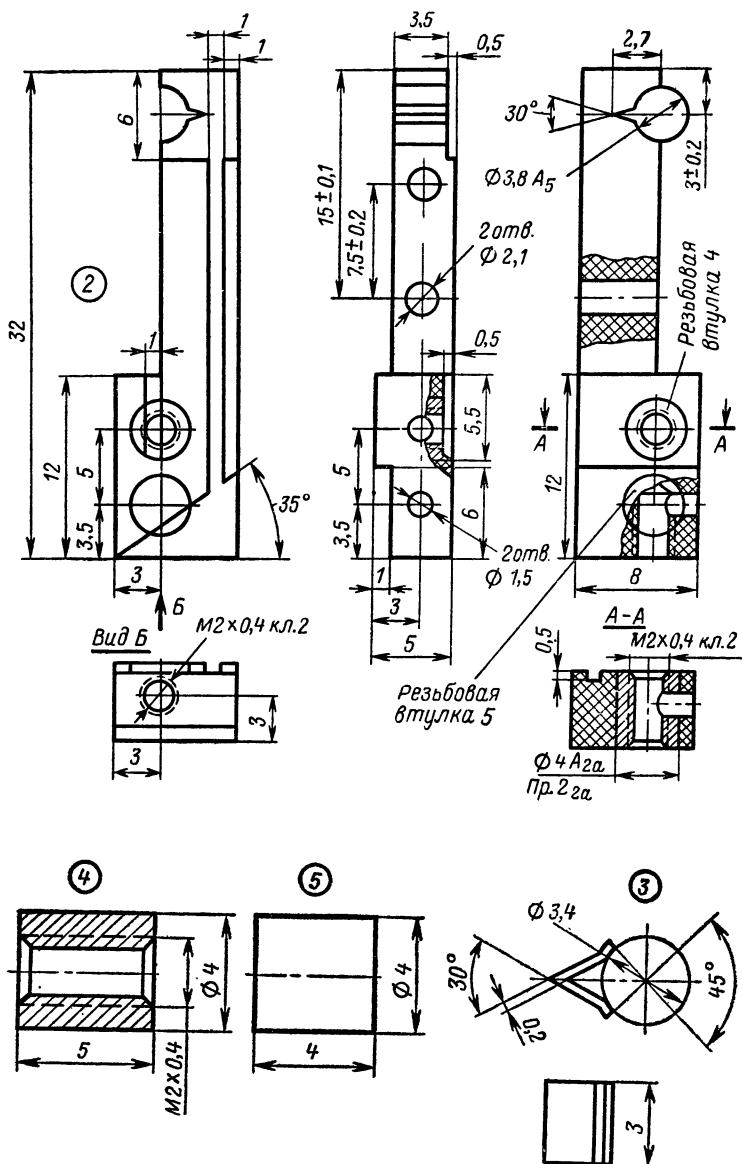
Чертежи корпуса фотодиодного датчика для распределителя Р119 автомобиля «Волга» ГАЗ-21.
